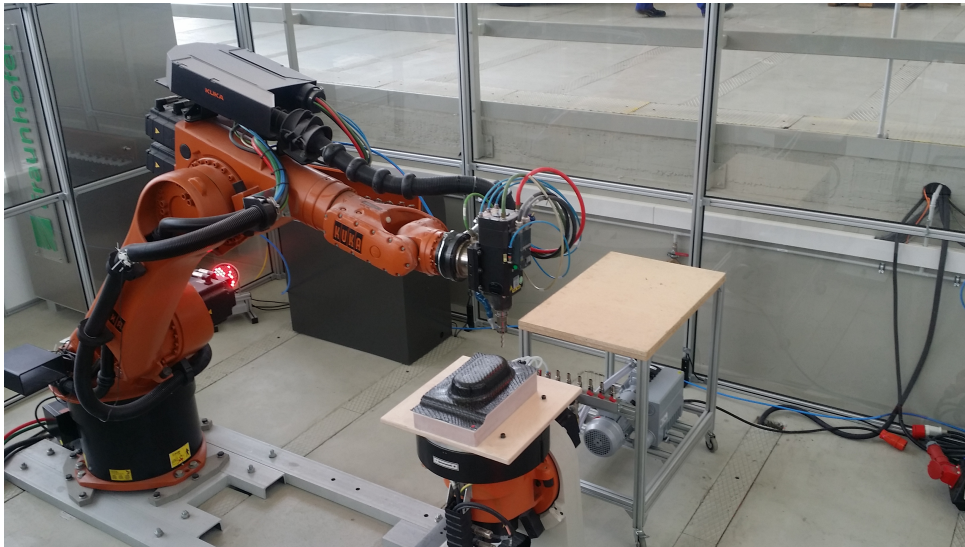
Roboterzelle im Versuchsfeld des Instituts für Werkzeugmaschinen und Fabrikbetrieb
